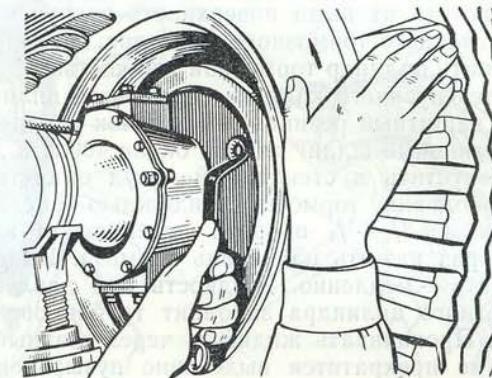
Регулировка зазоров между колодками и тормозным барабаном переднего колеса
